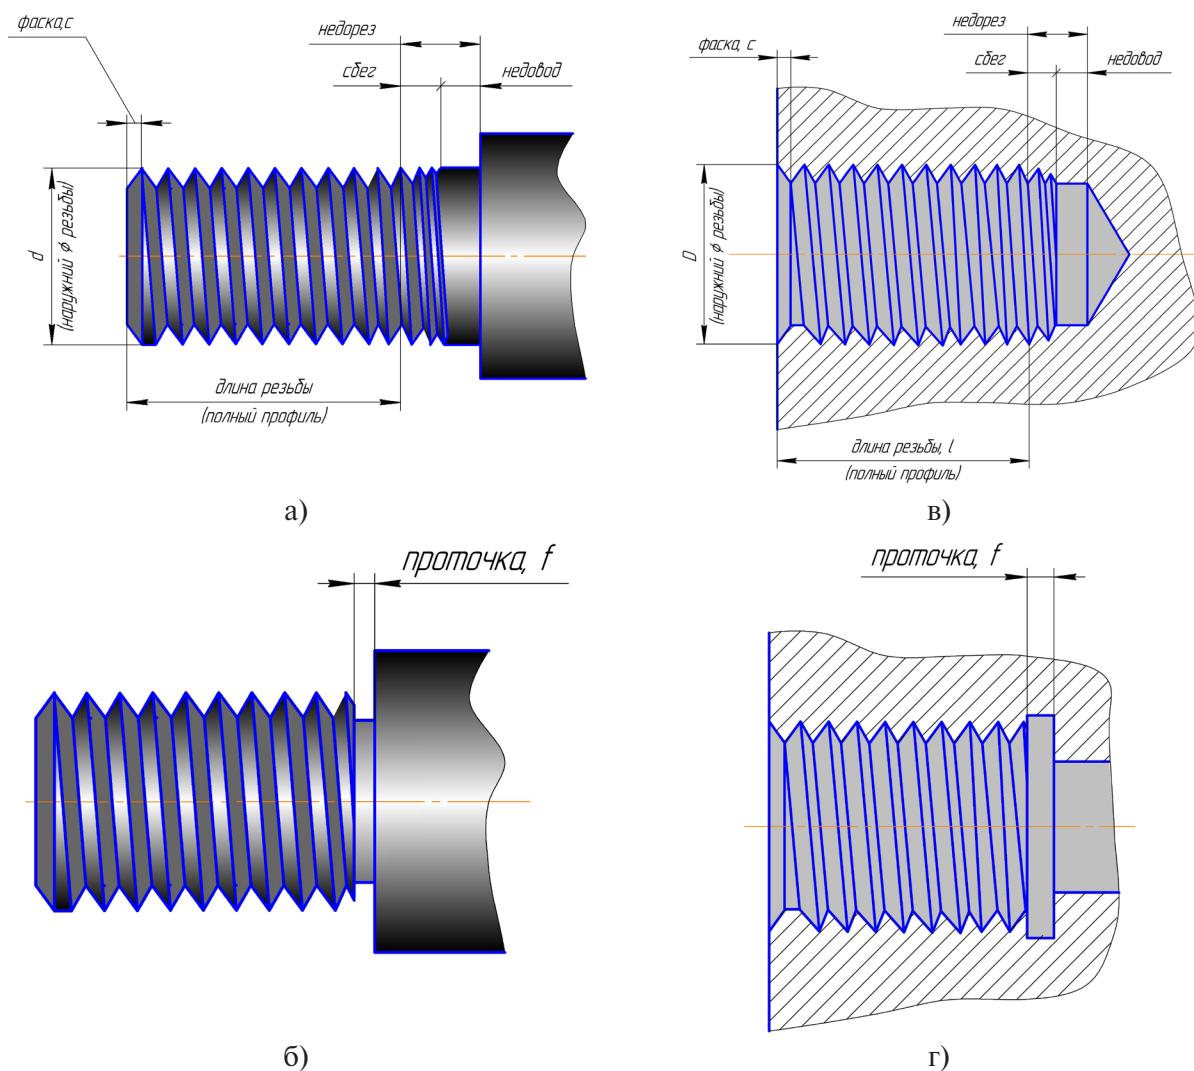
Конструктивные элементы резьбы: а, б — на стержне; в, г — в отверстии
